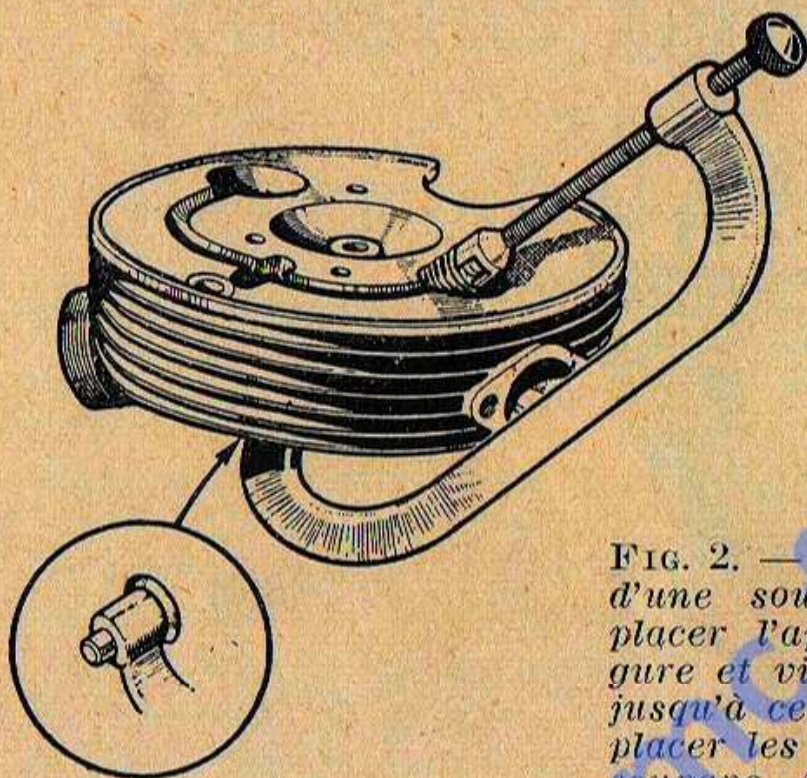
Montage - Démontage d'une soupape. Au remontage placer l'appareil suivant la figure et visser le bouton moleté jusqu'à ce qu'il soit possible de placer les clavettes de queue de soupape. Avant de redévisser le bouton moleté, s'assurer que les ressorts et les clavettes sont bien à leurs places respectives.
